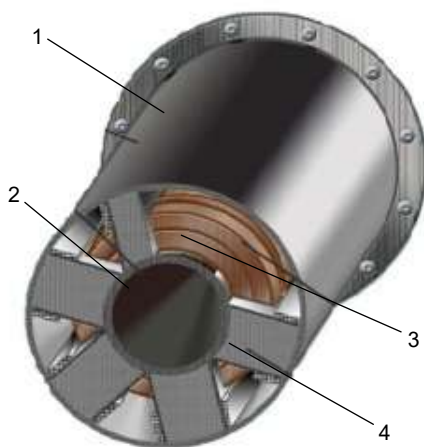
Общий вид низкочастотного магнитного перистальтического насоса. 1 – корпус, 2 – рабочий канал, 3 – обмотка, 4 – внешний магнитопровод.
